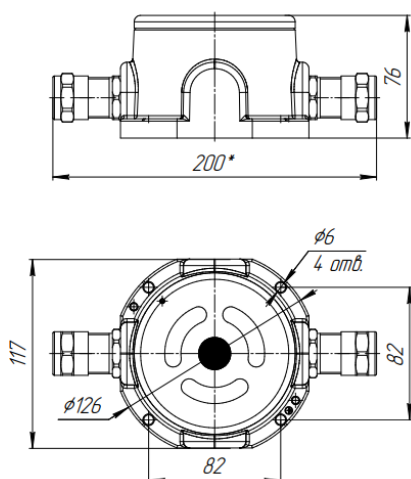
Габаритные и присоединительные размеры, корпус из нержавеющей стали (Н).
